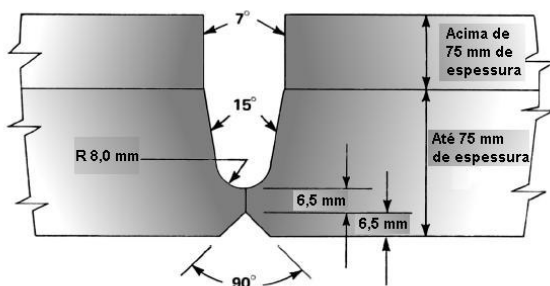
Procedimento de soldagem multipasse para peças com espessura com um único arame e cobre-juntas não consumível
